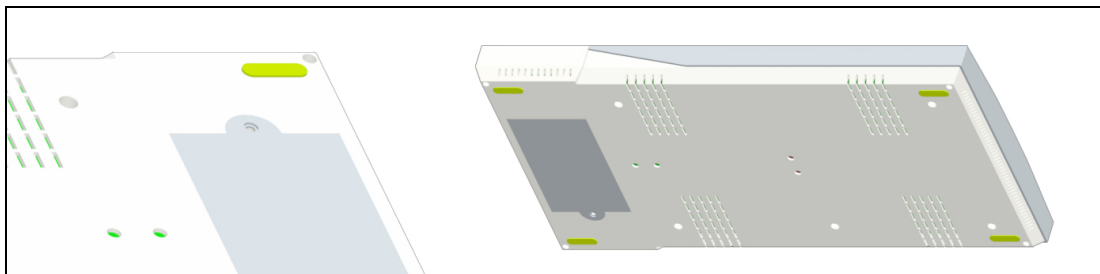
>1. Detalle del sistema antideslizante.
